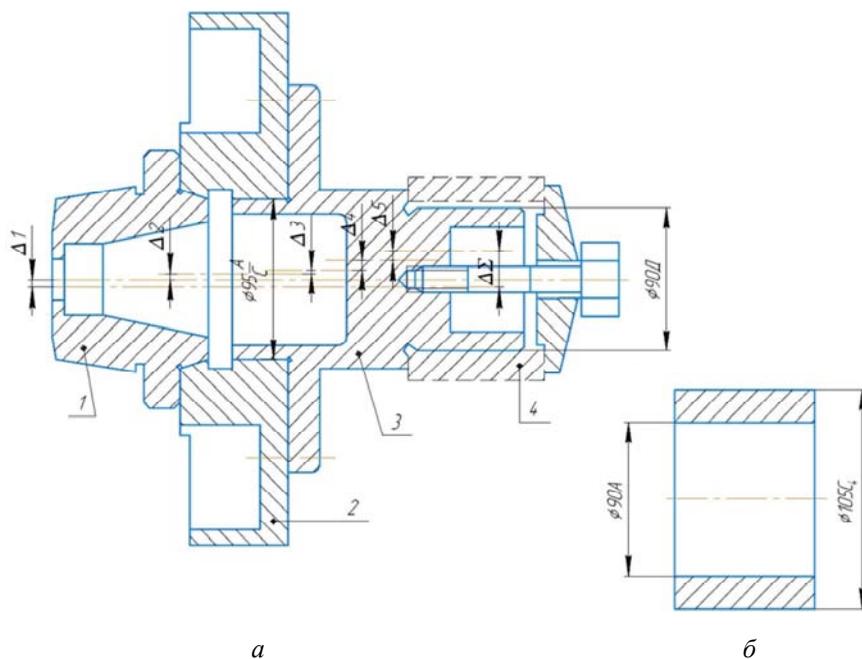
Схема установки детали на планшайбе с цилиндрическими наладками (а) и обрабатываемая деталь (б):
